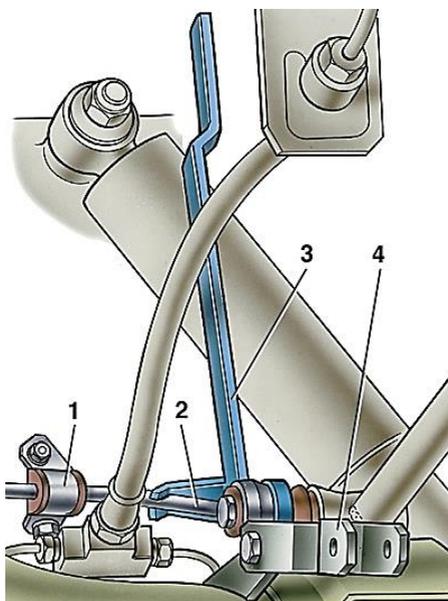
Установка приспособления 67.7820.9518 для регулировки регулятора давления задних тормозов:
